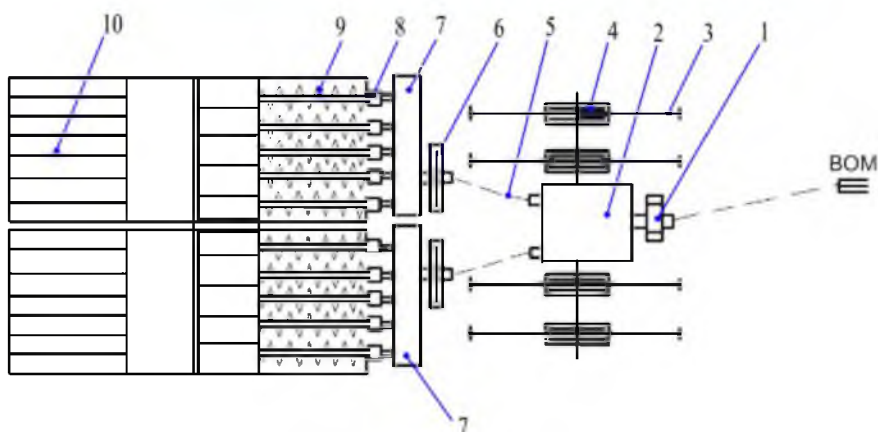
Кинематическая схема машины МТК-1,6: 1 – муфта; 2 – редуктор привода фрез; 3 – фрезы; 4 – фрикционные муфты фрез; 5 – карданные валы; 6 – фрикционные муфты; 7 – редукторы привода винтов пресса; 8 – муфты; 9 – многовинтовой пресс; 10 – формующий блок
